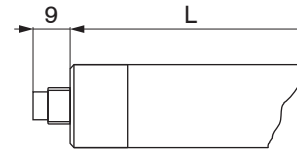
Wegsensor Typ - SA mit axialer Steckverbindung
